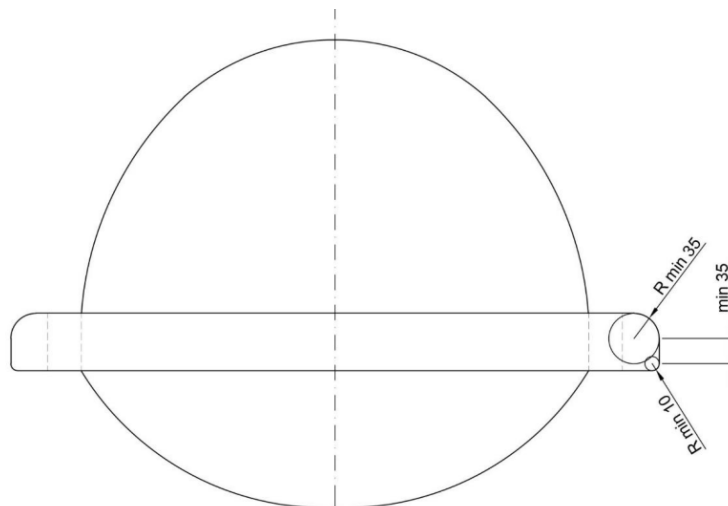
Vista frontal cotada (mm) do trenó [21]
